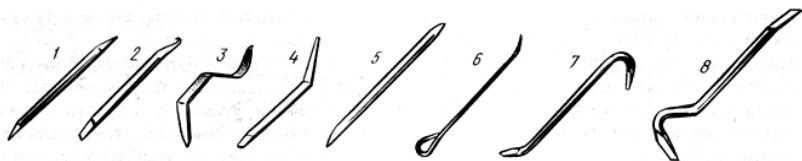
Рычаги и прижимы для исправления вмятин: 1 – рычаг для исправления дефектов штамповки; 2 – рычаг для рихтовки крыльев после окраски; 3 – рычаг-прижим; 4 – рычаг для исправления вмятин; 5 – рычаг пластинчатый для исправления вмятин в труднодоступных местах; 6 – рычаг для исправления различных дефектов; 7 – рычаг для предварительной правки; 8 – рычаг для устранения больших деформаций
